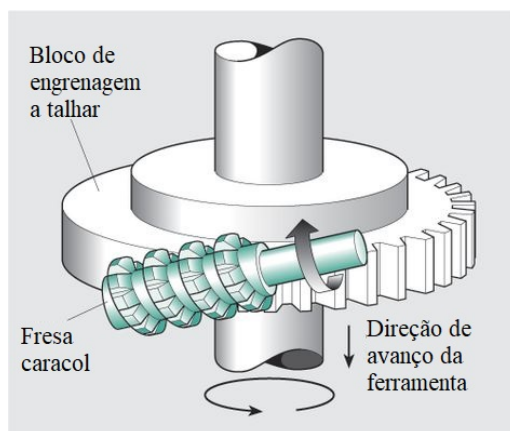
Operação de maquinagem de engrenagens por fresa-mãe ou ferramenta tipo caracol (Adaptado de [23]).
